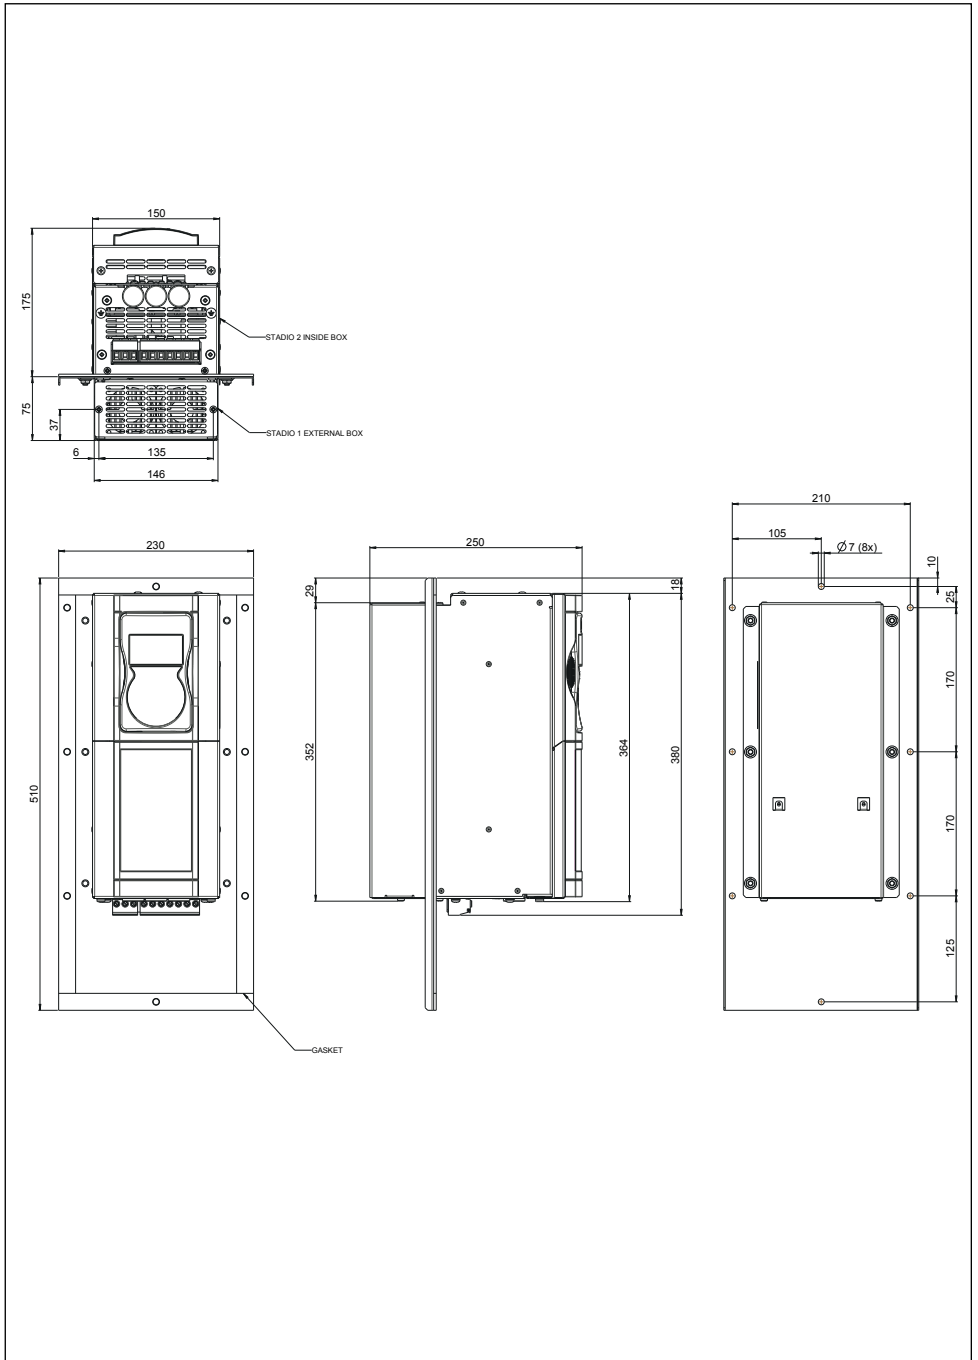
Размеры для типоразмера 3 (ADV200-...-EHR)
